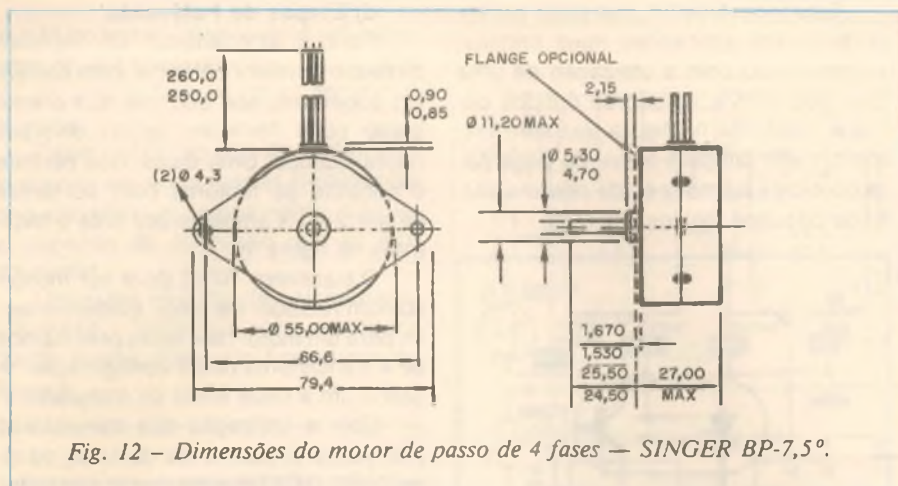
Dimensões do motor de passo de 4 fases - SINGER BP-7,5°.
